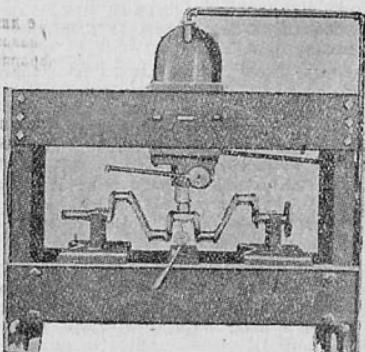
Правка коленчатого вала прессом с выверкой по индикатору
